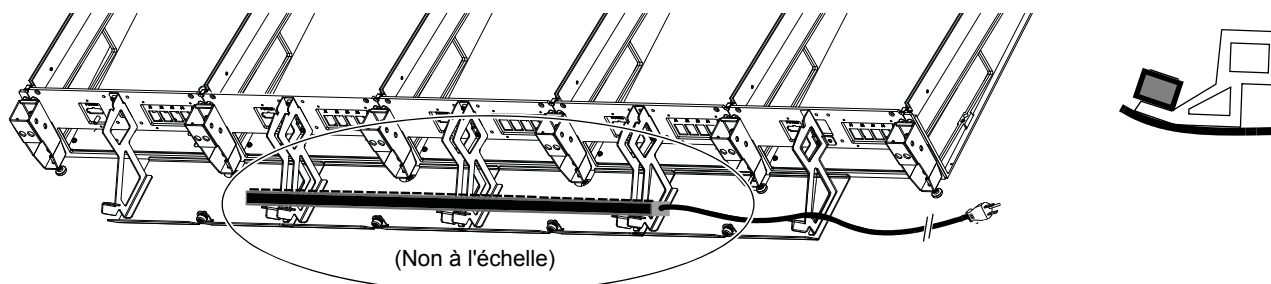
Placement de la multiprise sur les supports des panneaux arrière (vue arrière à gauche, vue de côté à droite)
